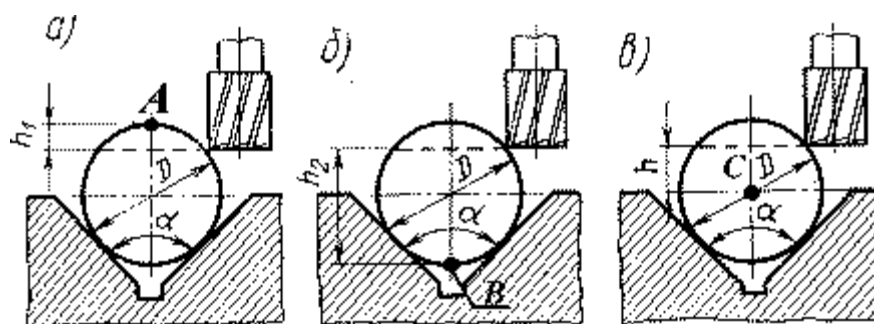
Вимірювальні бази для обробки валу в призмі
